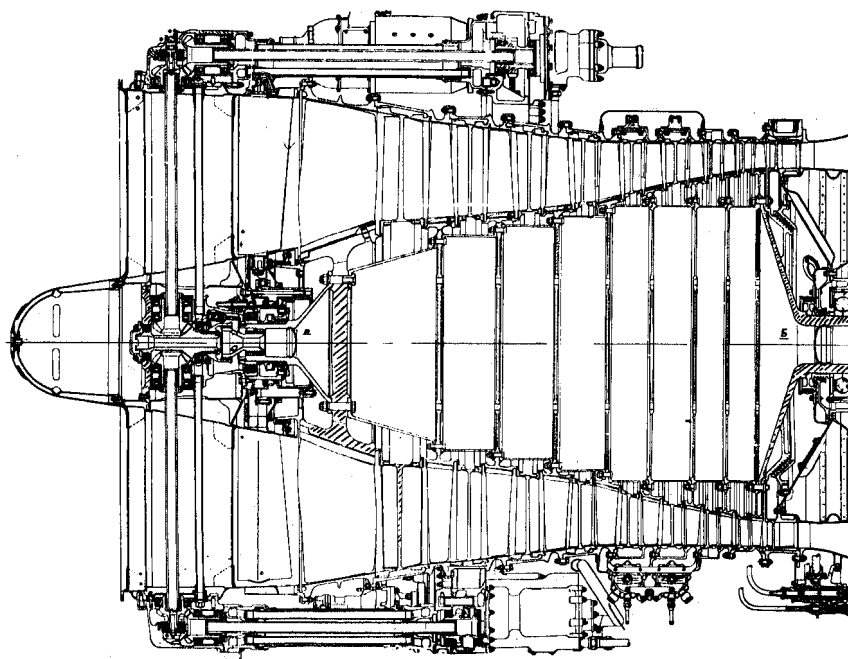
Разрез осевого компрессора турбореактивного двигателя ВД-7М с проточной частью комбинированного типа
